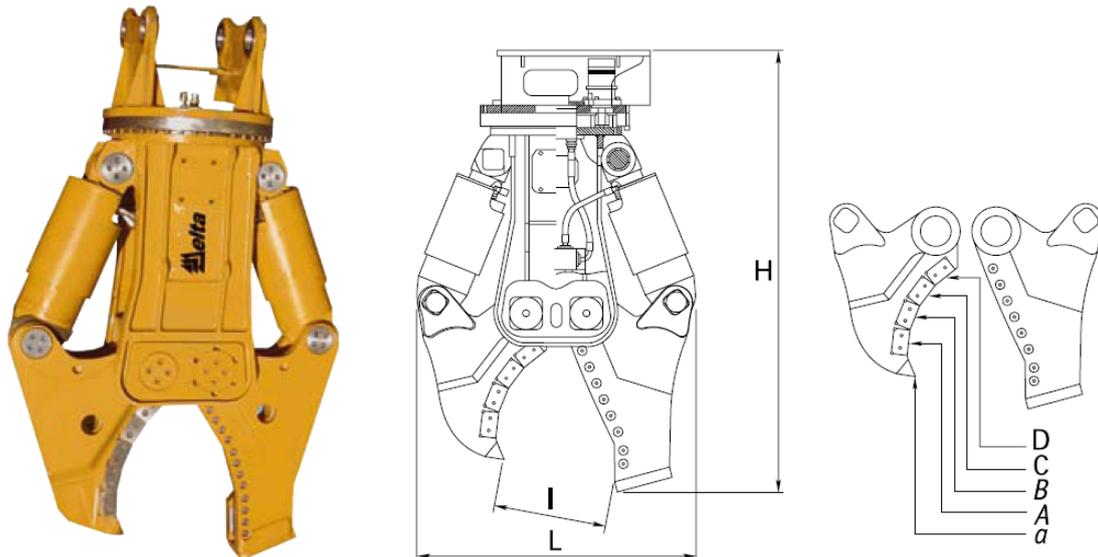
Гидроножницы для резки металла полноповоротные (мультипроцессор)
